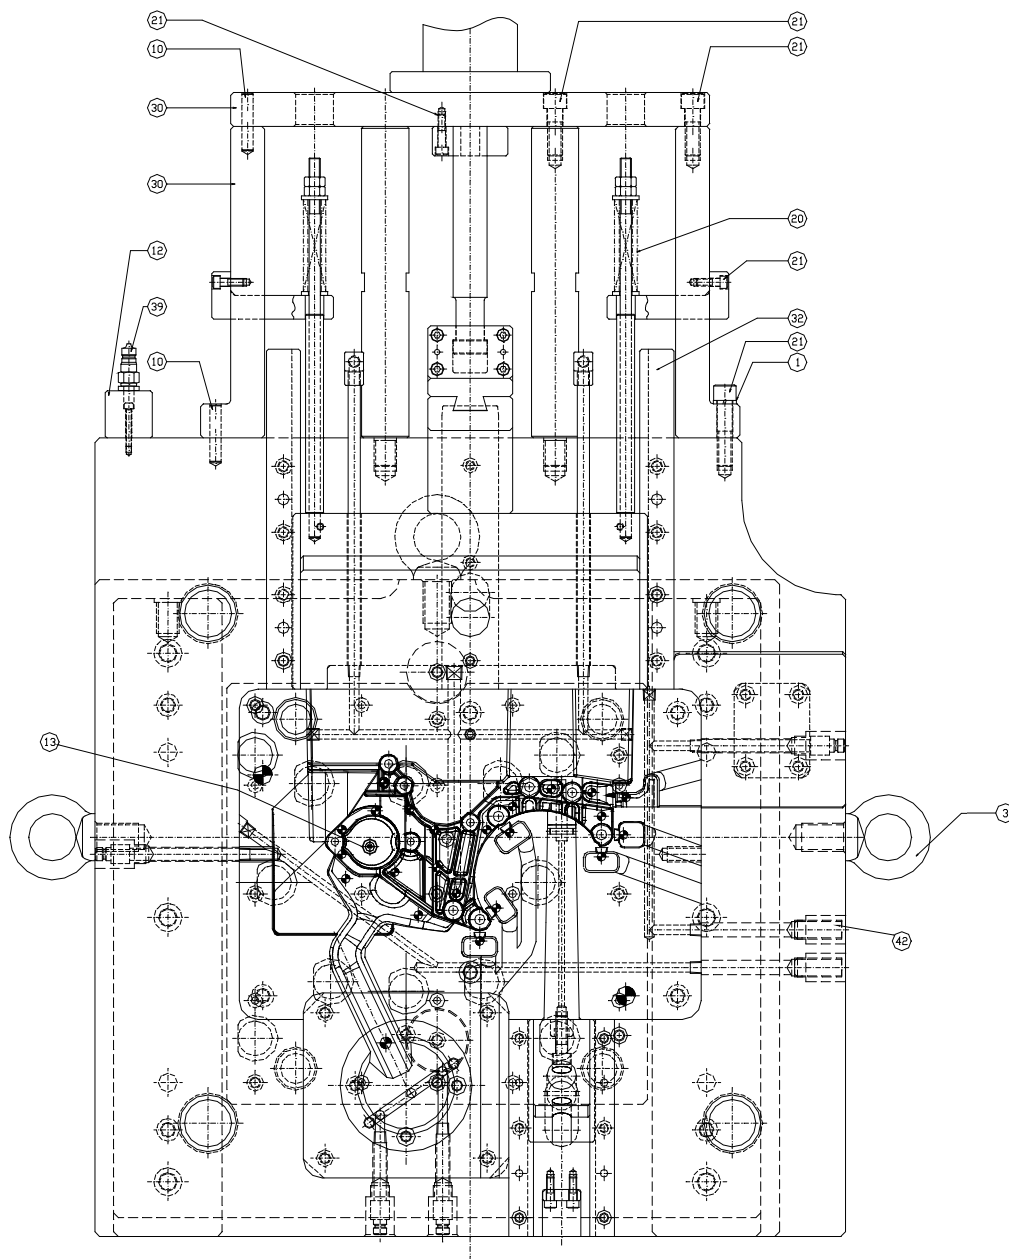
Desenho de conjunto do molde (vista de frente) (4)
